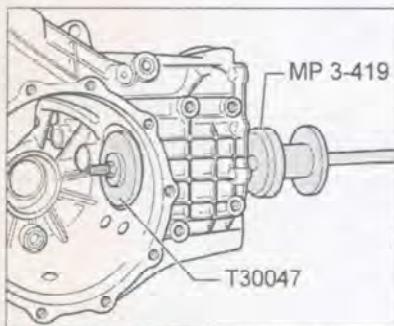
Извлечение наружной обоймы большого роликоподшипника.
